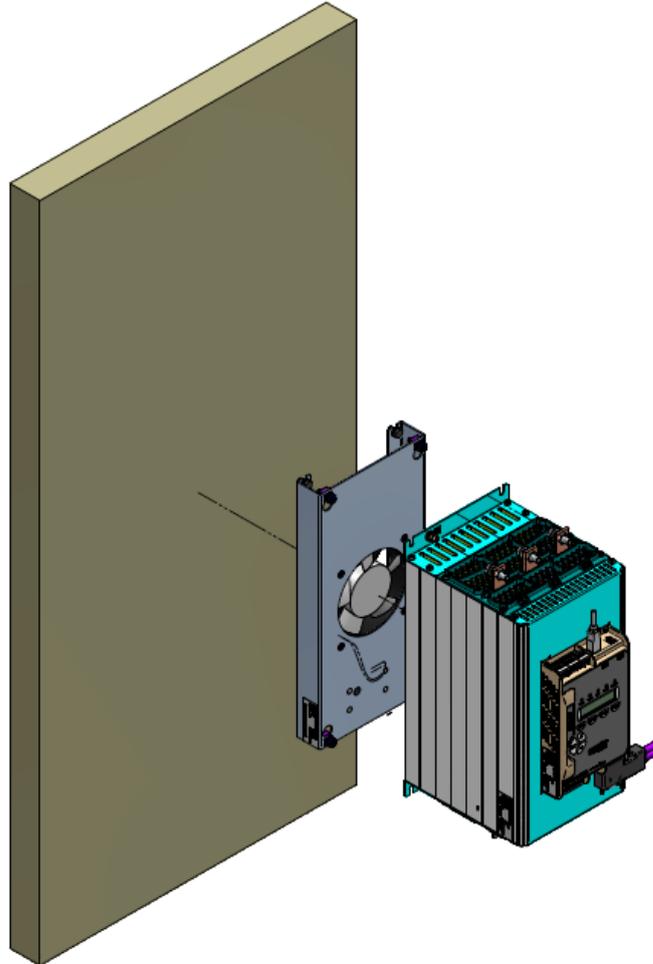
Installation d'un ventilateur (tailles A, B et C)
